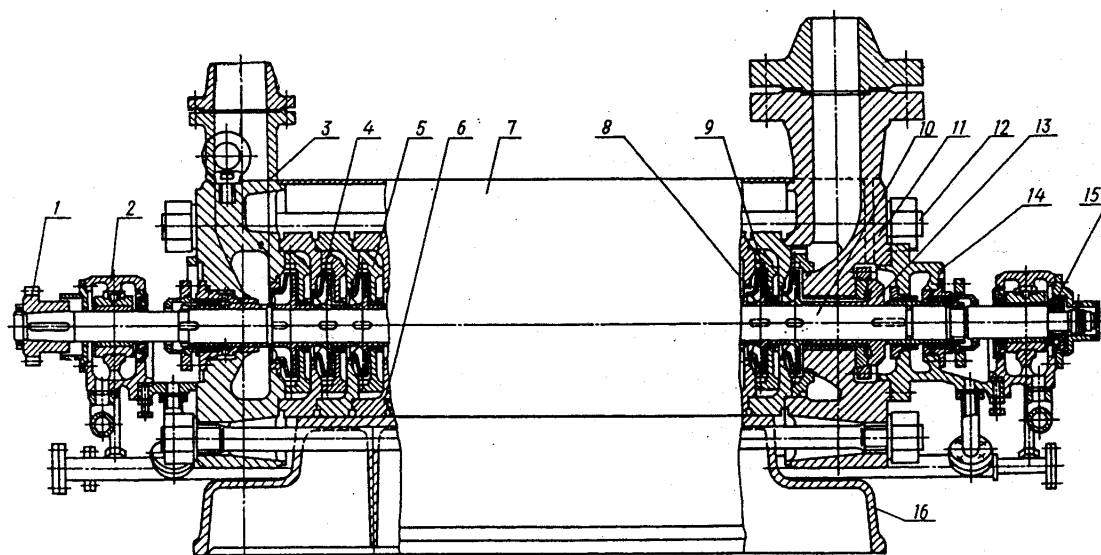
Конструктивна схема агрегата ЦНС 180-1900 в розрізі,
